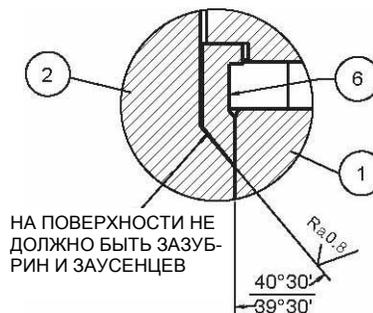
Угол посадки крышки (см. Рис. 10, Деталь В)
